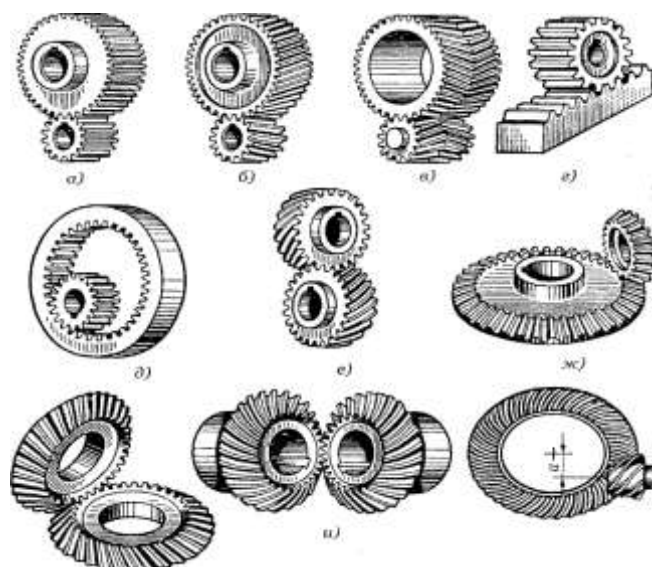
Виды зубчатых передач: *а, б, в* — цилиндрические зубчатые передачи с внешним зацеплением; *г* — передача винт-гайка; *д* — цилиндрическая передача с внутренним зацеплением; *е* — зубчатая винтовая передача; *ж, з, и* — конические зубчатые передачи; *к* — гипоидная передача
